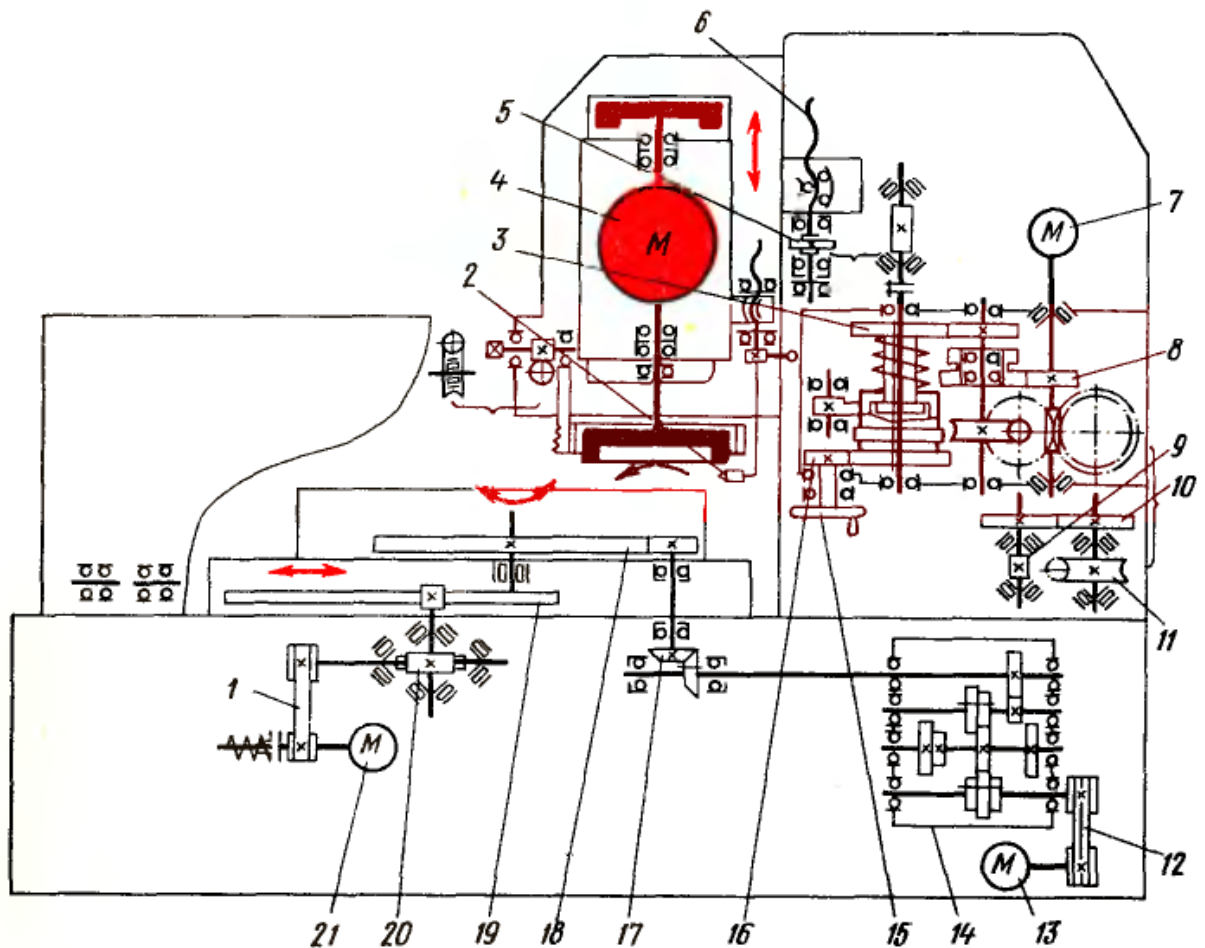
Кинематическая схема станка с круглым столом и вертикальным шпинделем
